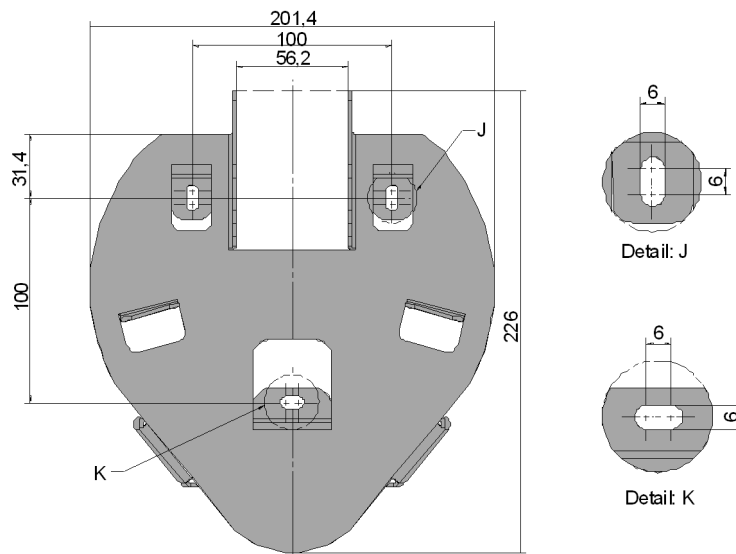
Frontansicht Wandhalterung KeTop WB090
